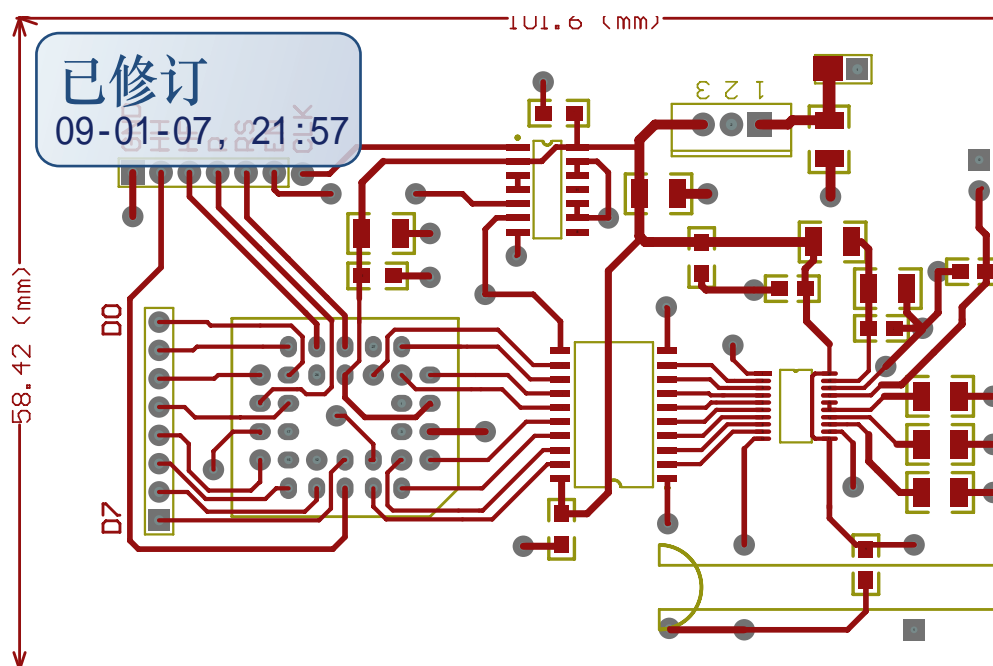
：高速 AD 转换与 FIFO 存储电路 PCB 板图
